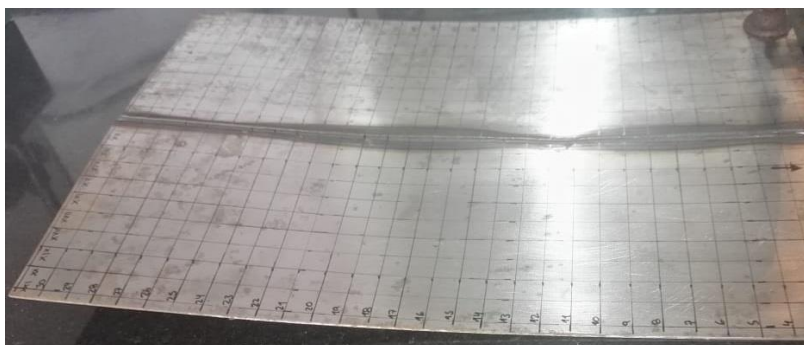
6 – Imagem final da chapa soldada pelo processo MAG.
